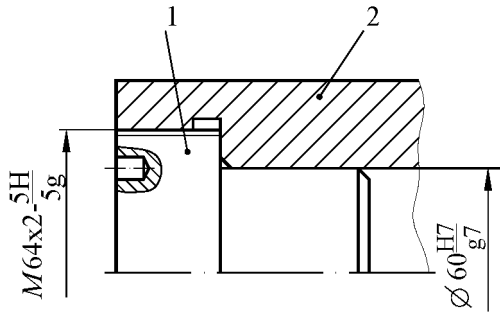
Сопряжение по гладкой и резьбовой поверхностям
